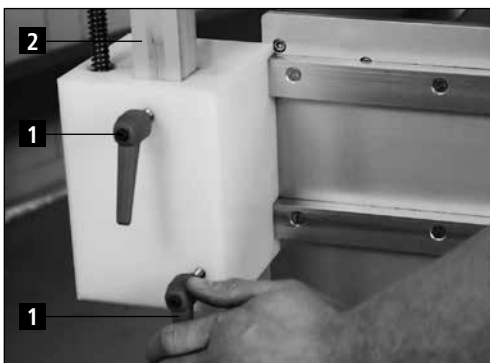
Messer auf Schleifscheibenmitte einstellen
